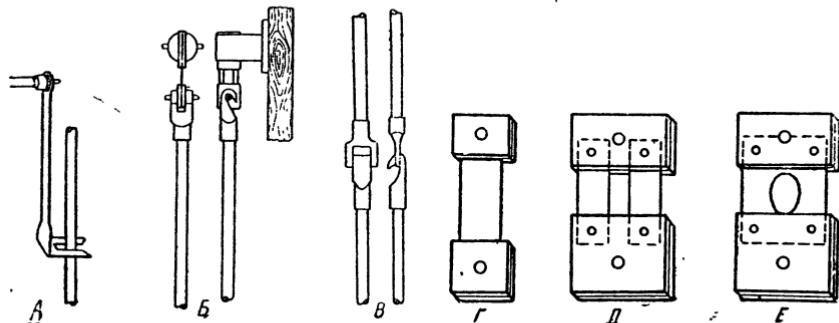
А—вилка маятника; Б—пружинный подвес маятника; В—маятник с составным стержнем; Г и Е—одинарный пружинный подвес
